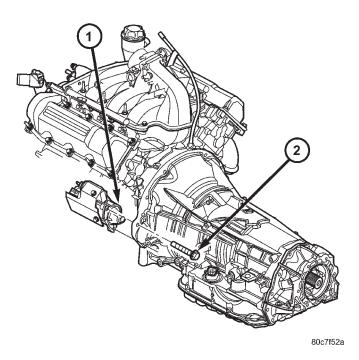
MOTOR DE ARRANQUE - 3.7L
